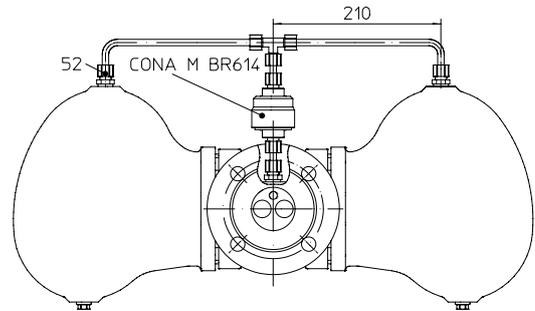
1 mit Flanschen - horizontale Einbaulage und äußere Entlüftung
